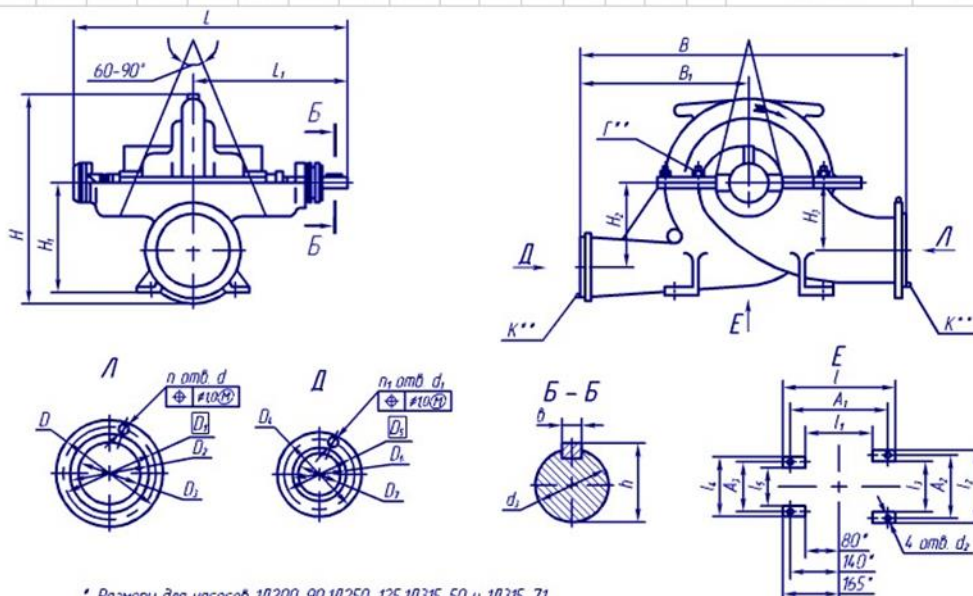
Габаритный чертеж насоса 1Д 630-90а
